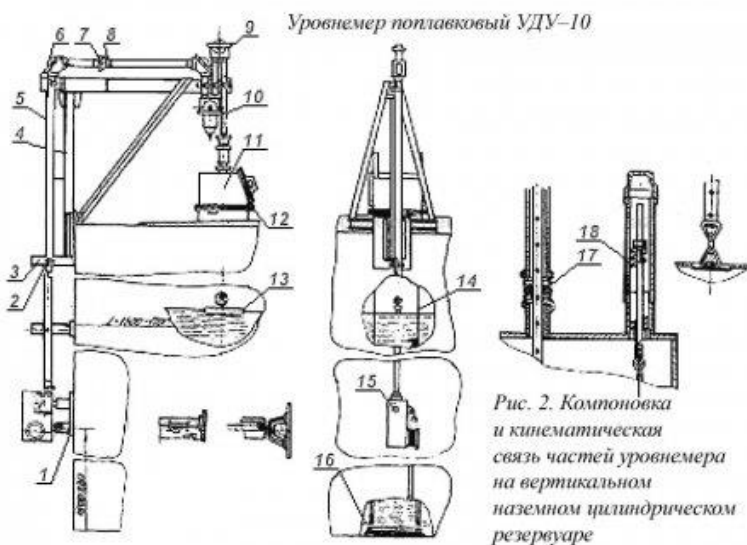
Компоновка и кинематическая связь частей уровнемера на вертикальном наземном цилиндрическом резервуаре
